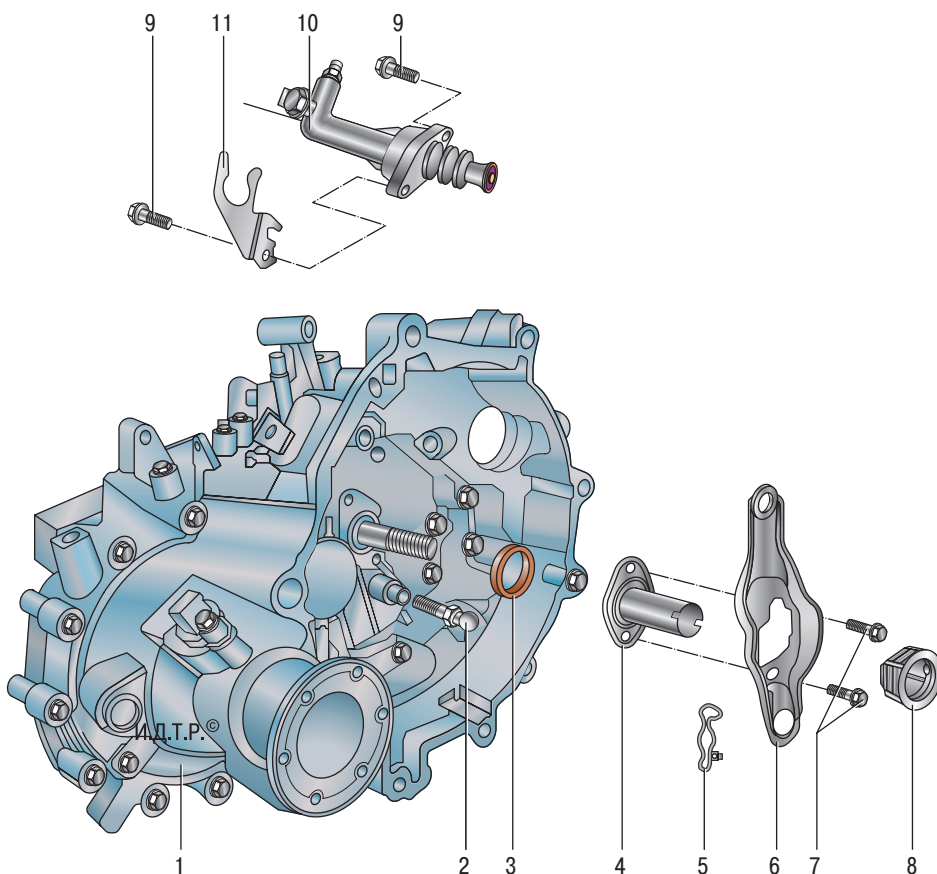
Механизм выключения сцепления: 1 – коробка передач; 2 – шаровая опора вилки выключения сцепления; 3 – сальник первичного вала коробки передач; 4 – направляющая втулка; 5 – фиксирующая пружина вилки выключения сцепления; 6 – вилка выключения сцепления; 7 – болты крепления направляющей втулки; 8 – подшипник муфты выключения сцепления; 9 – болт крепления рабочего цилиндра; 10 – рабочий цилиндр привода выключения сцепления; 11 – кронштейн крепления трубопровода
